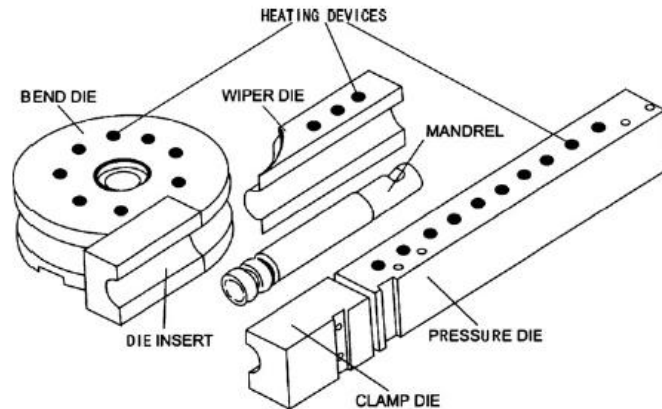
Setup del sistema di draw bending con elementi riscaldanti inseriti negli stampi e mandrino per guidare la piega. [15]
